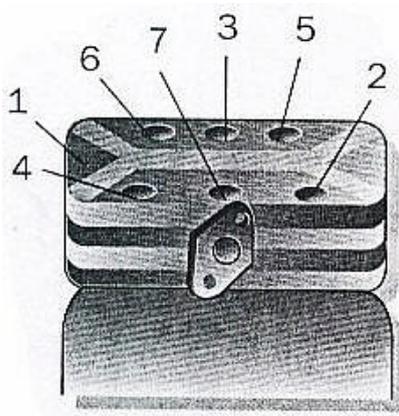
Retiragem do cabeçote e placa de válvulas.
